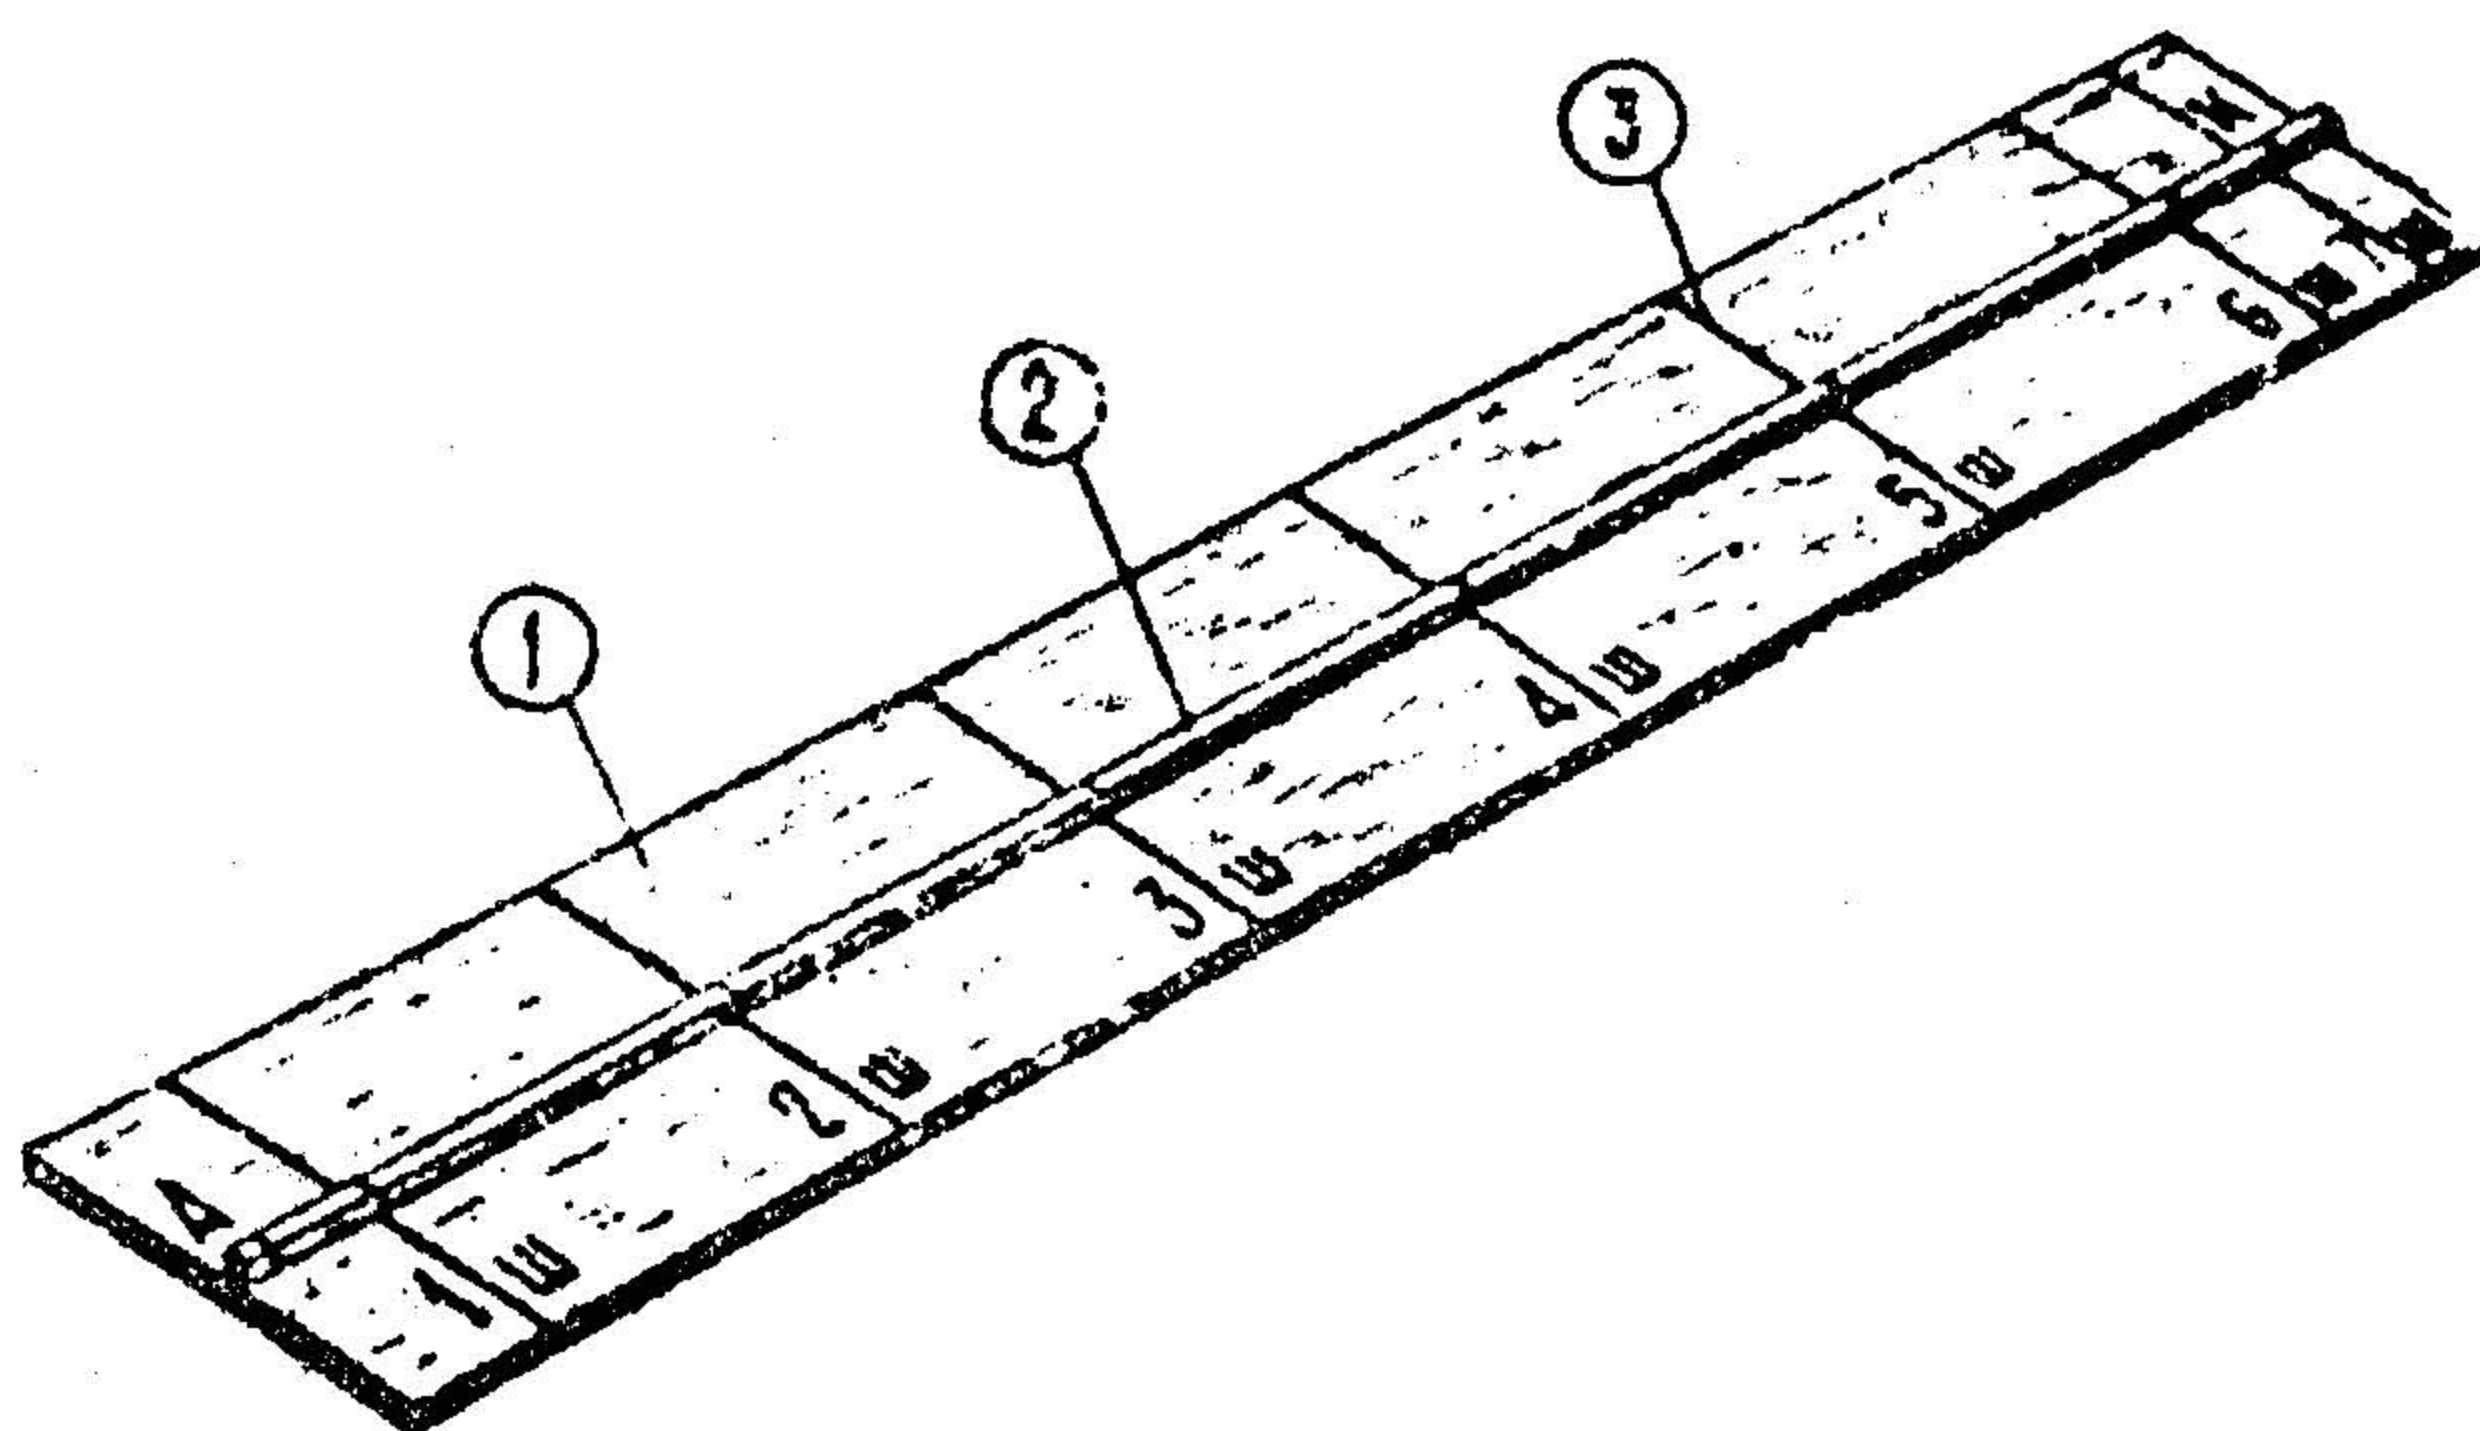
Разметка шпангоутов: 1 — фанера; 2 — плавовая рейка; 3 — место шпангоута
